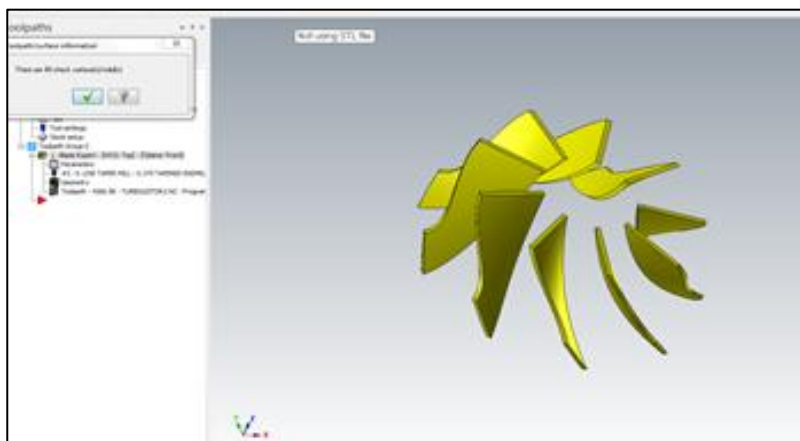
Enlace del maquinado para los álabes del turbo [fuente propia]
